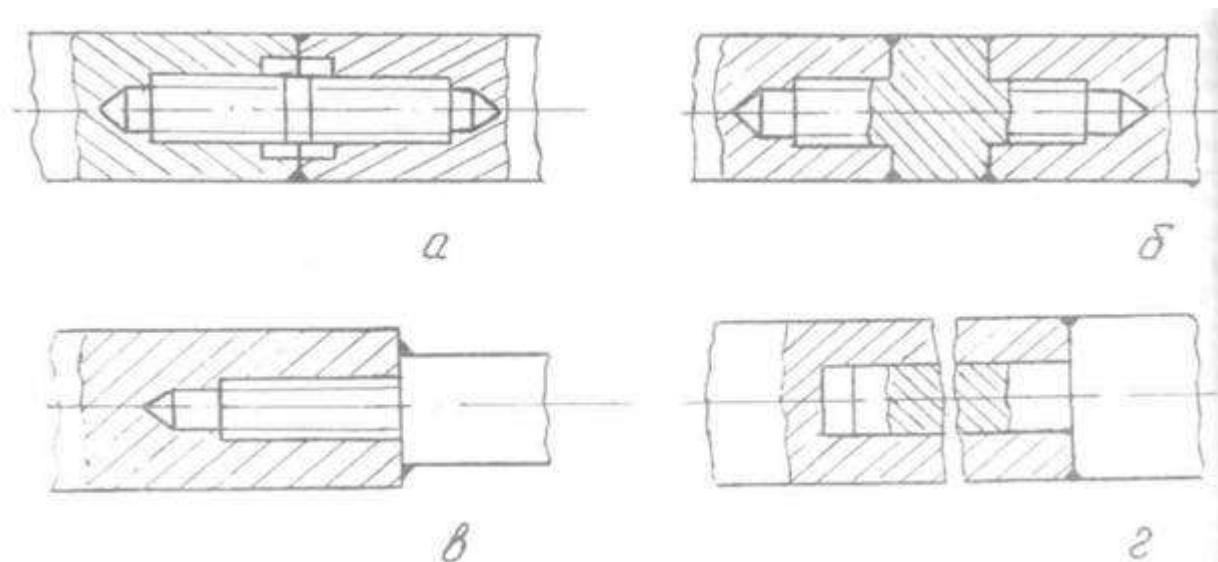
Способы восстановления поломанных валов с применением сварки при помощи: шпильки (а), вставки (б), надставки (в,г).
